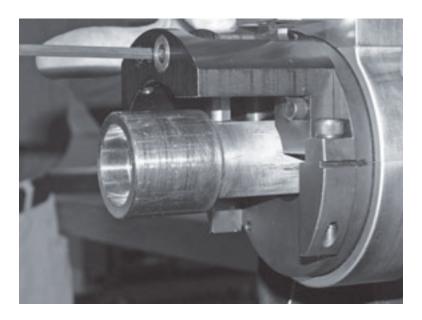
Réglez l'outillage proche de la soudure avant de commencer la coupe.
